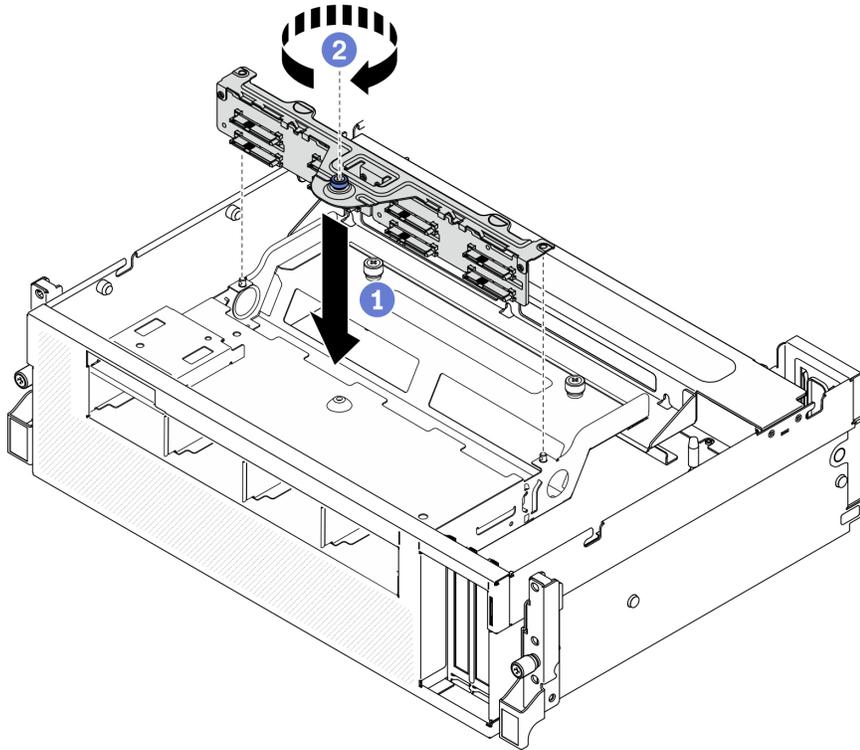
Installation du module du fond de panier d'unité 2,5 pouces
